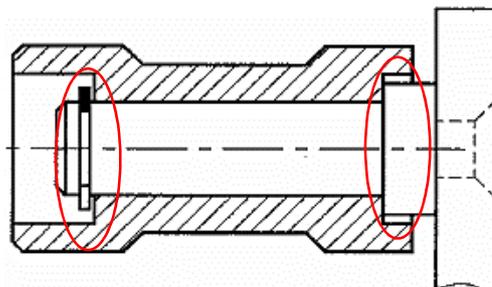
Guidage en rotation par contact direct, arrêts axiaux : épaulement et anneaux élastiques.
